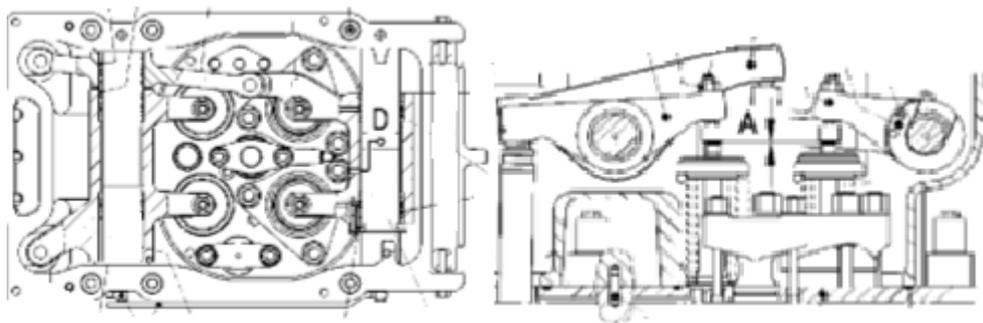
Vista de perfil y en planta de la caja de balancines.
